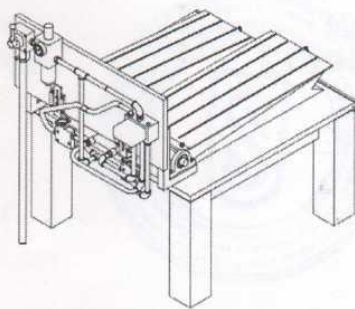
Габаритный чертеж привода (АхБ=1025х860)
